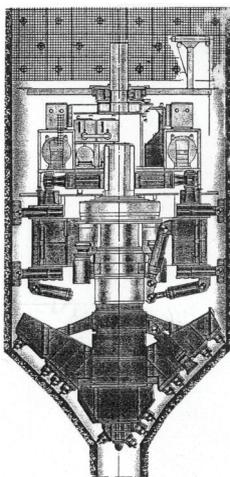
Общий вид ротора бурового агрегата (ФРГ)
